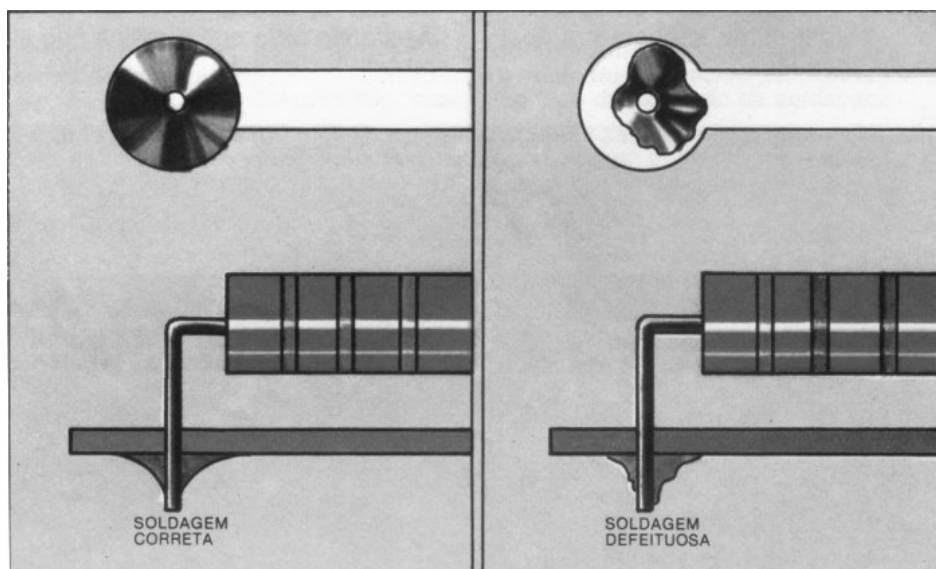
Exemplos de soldagem correta e defeituosa (extraído de [1]).
